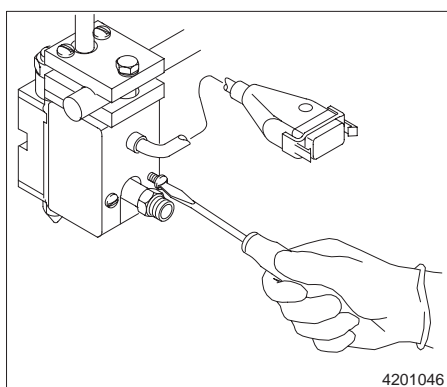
Vis du capot recouvrant le corps du pistolet
